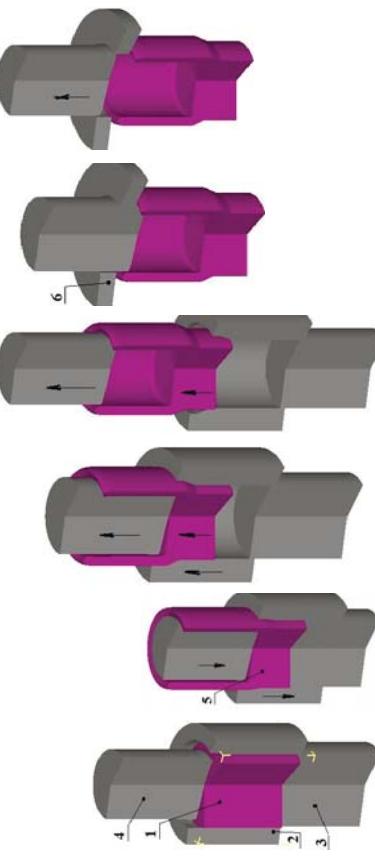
Розрахункові схеми в розрізі для ZVR заготовки діаметром $D_o=46$ мм
